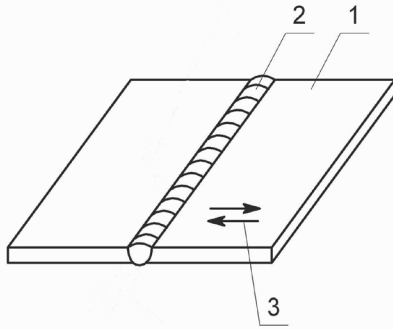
Схема сварки образцов: 1 – свариваемые пластины; 2 – сварочный шов; 3 – направление упругих колебаний
